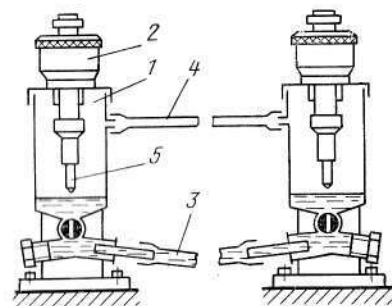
Гидростатический уровень: 1 — резервуар; 2 — микрометрическая головка; 3, 4 — прозрачные шланги для воды и воздуха; 5 — микрометрический уровень
